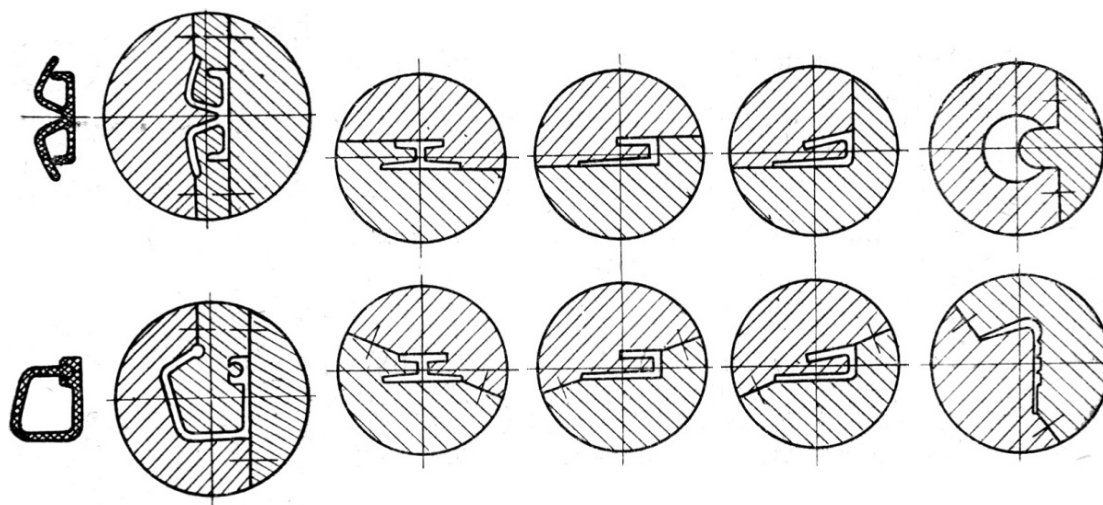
Примеры конструктивных схем матриц для некоторых изделий
